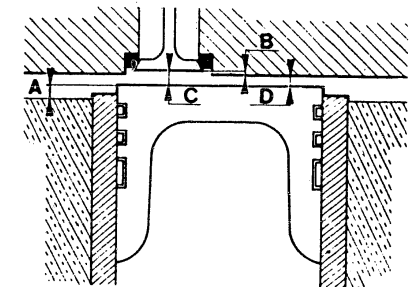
Dieselmotor J8S: Das Spaltmass D muss in der OT-Stellung des Kolbens mehr als 0,6 mm betragen. A = Kolbenüberstand - B = Rückstehmass des Ventiltellers - C = Ventilhub bei ausgebaute Feder.
